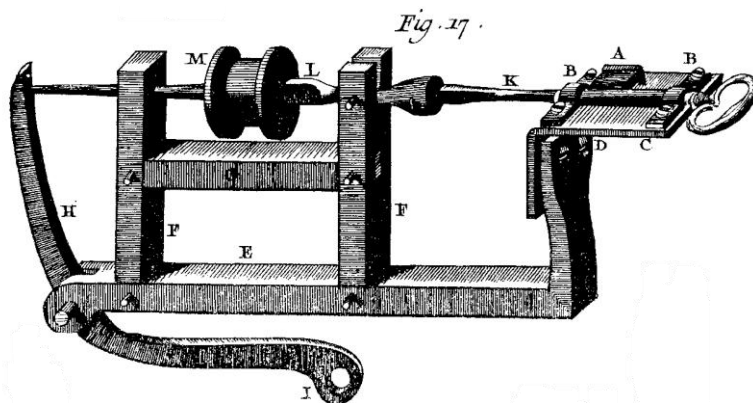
, Frees (A) gemonteerd op de boormachine, Fig. 90, boormachine, Fig. 91, Strijkstok of drillboog met houten handvat en zijn darmtouw.¹³⁵
